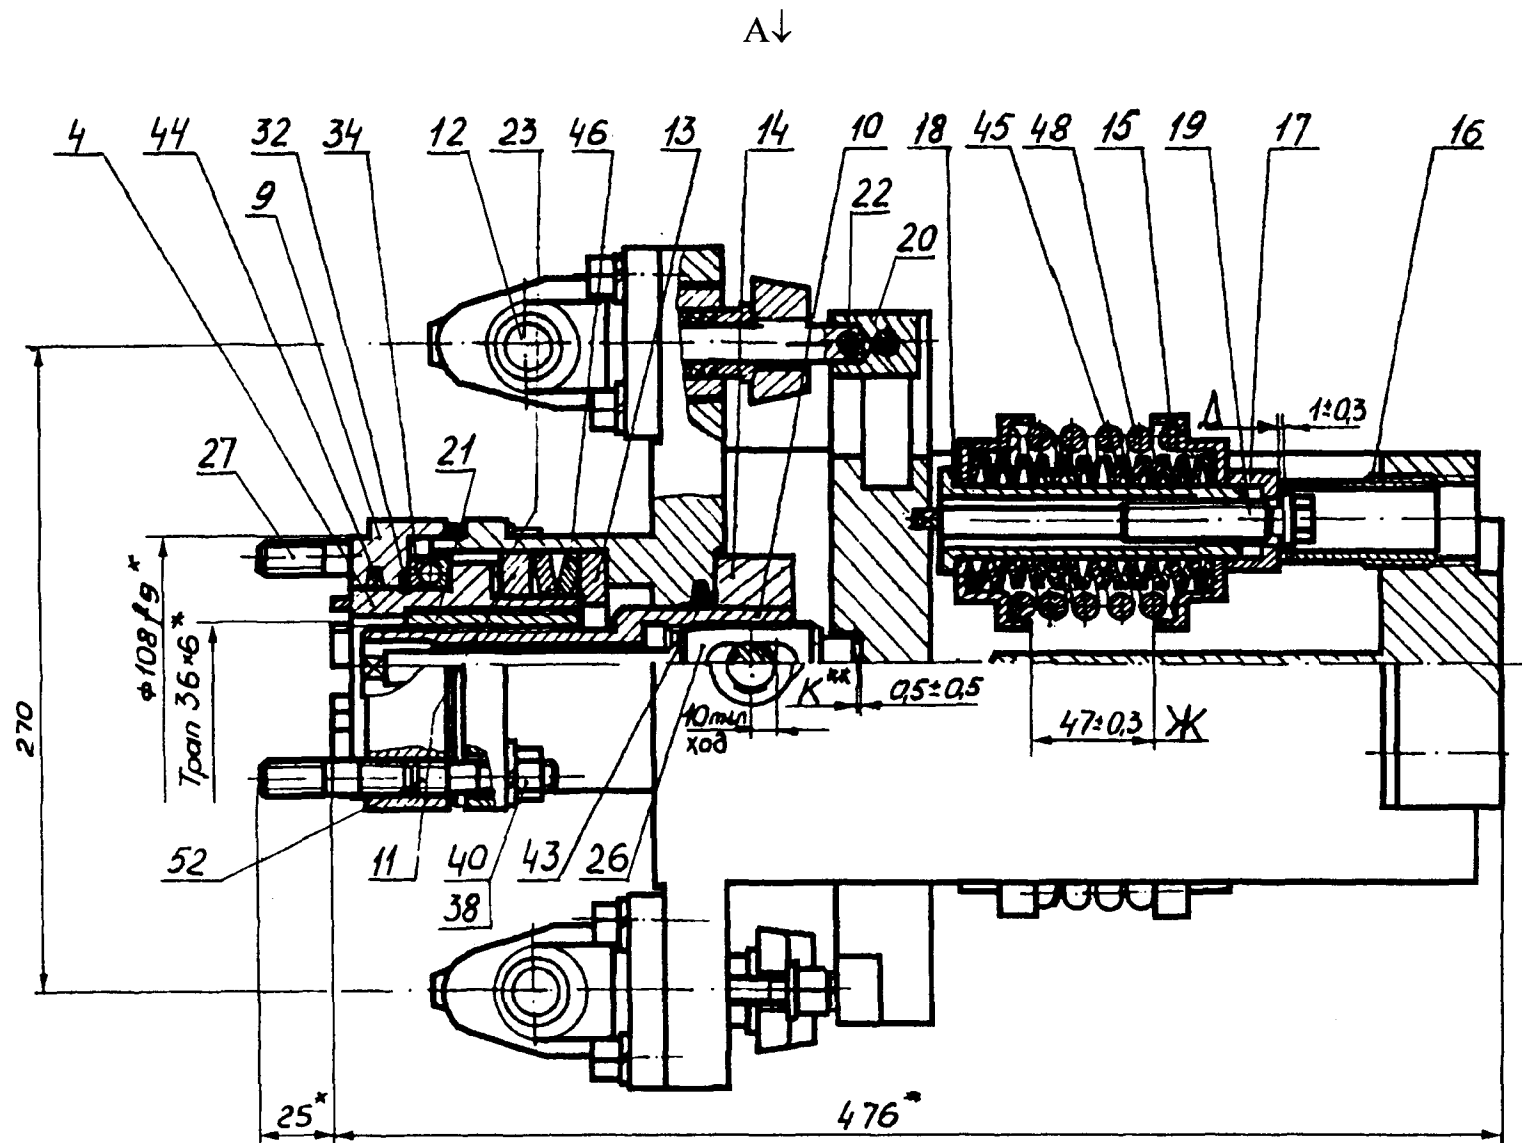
Общий вид механизма привода управления аварийной системы
